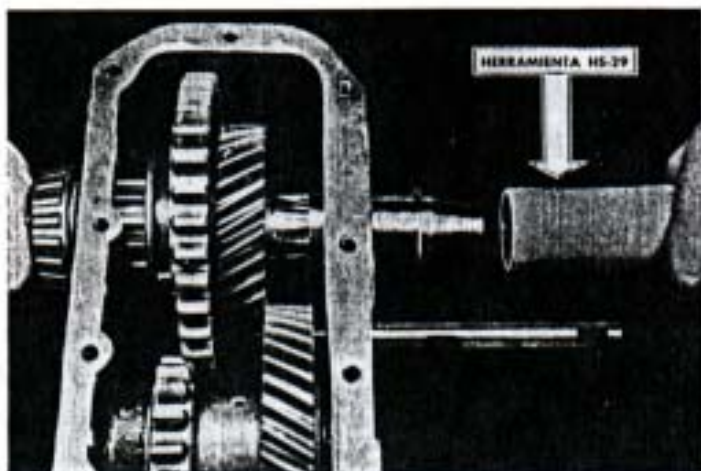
Instalando el aro retén del engranaje del eje principal, con la herramienta HS-29.
